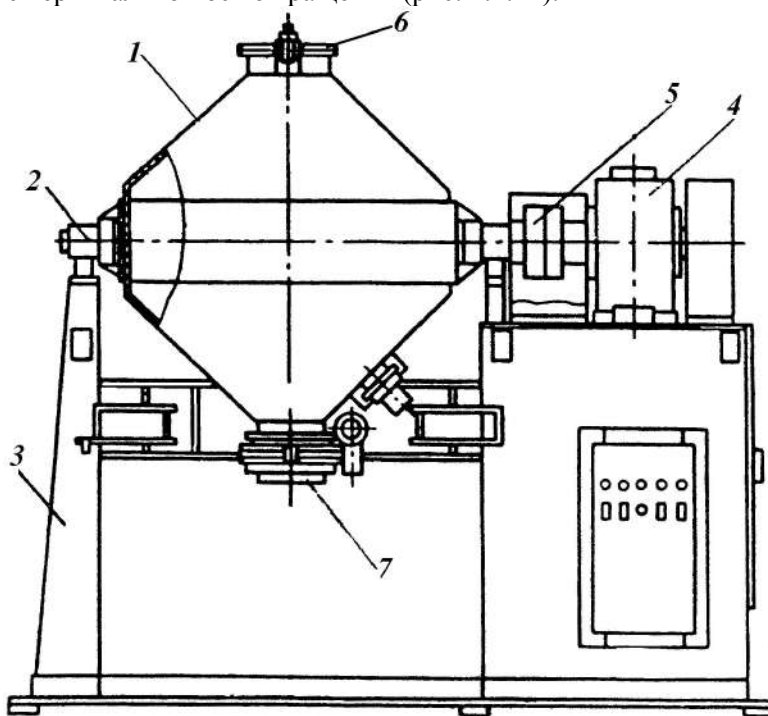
Смеситель барабанный биконический БК: 1 – корпус; 2 – цапфа; 3 – стойка; 4 – редуктор; 5 – муфта; 6 – загрузочный люк; 7 – выгрузочный патрубок.
